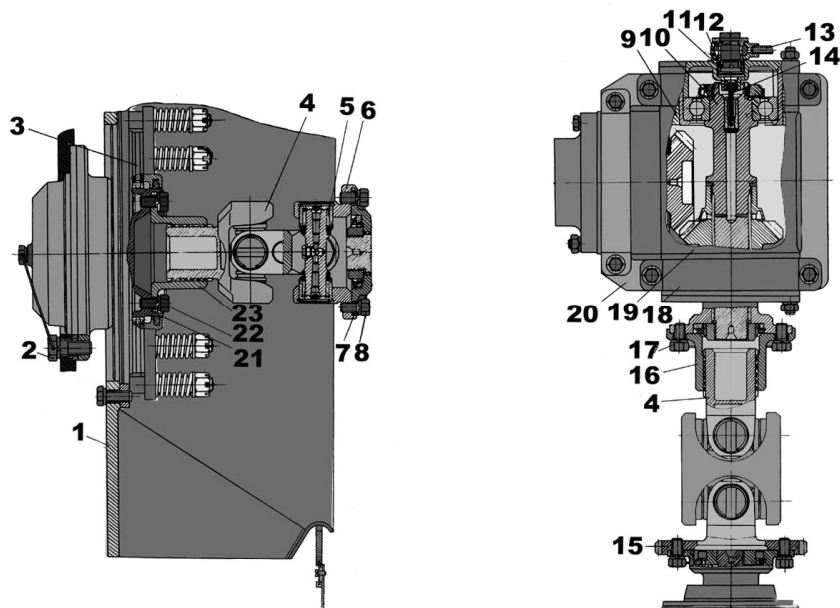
Привод вентилятора: 1 – вентилятор; 2 – болт крепления фрикциона вентилятора; 3 – фрикцион вентилятора; 4 – вилка кардана; 5 – игольчатые подшипники; 6 – вилка кардана; 7 – фланец конического редуктора; 8 – болт крепления; 9 – картер конического редуктора; 10 – вал; 11 – предохранительный фильтр; 12 – штуцер подвода масла для смазки; 13 – трубопровод; 14 – переходная втулка; 15 – вилка кардана с зубчатым венцом; 16 – муфта конического редуктора; 17 – болт крепления; 18 – наметка; 19 – конический редуктор; 20 – кронштейн; 21 – ведущая ступица фрикциона; 22 – болт крепления; 23 – муфта ведущей ступицы
